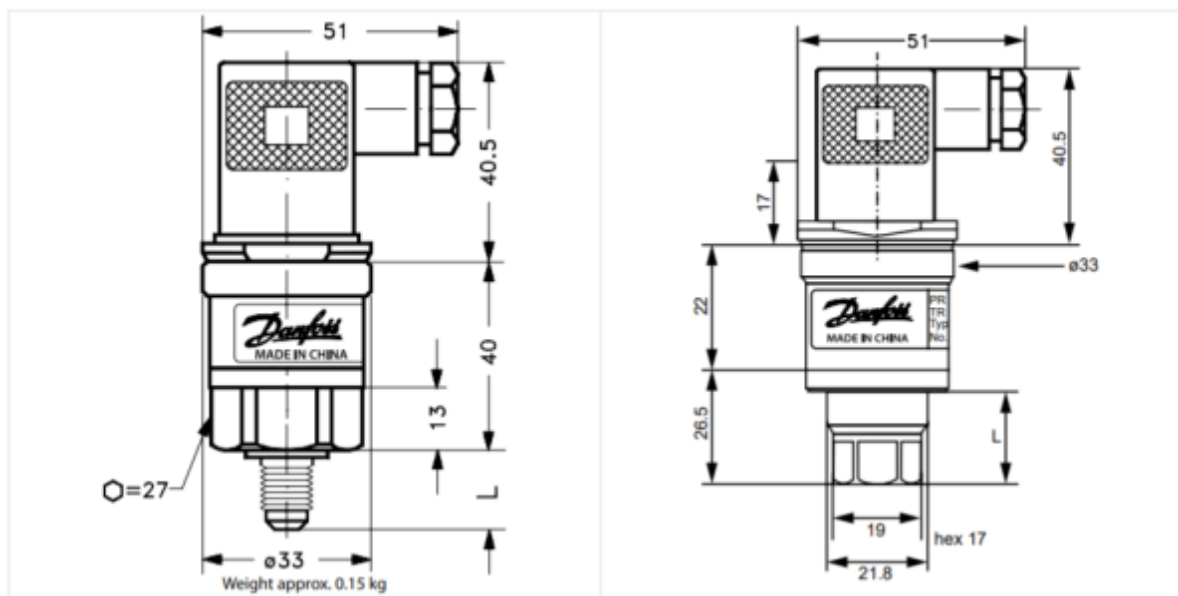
Габаритные размеры преобразователя давления AKS 32R
